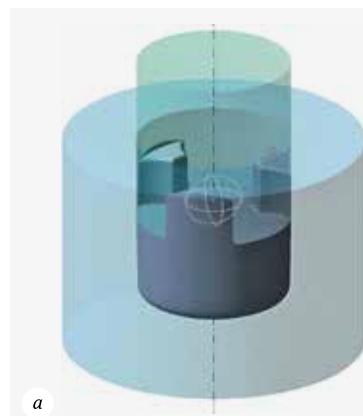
Штамповка корпуса муфты из алюминиевого сплава АД35: а – компьютерное
